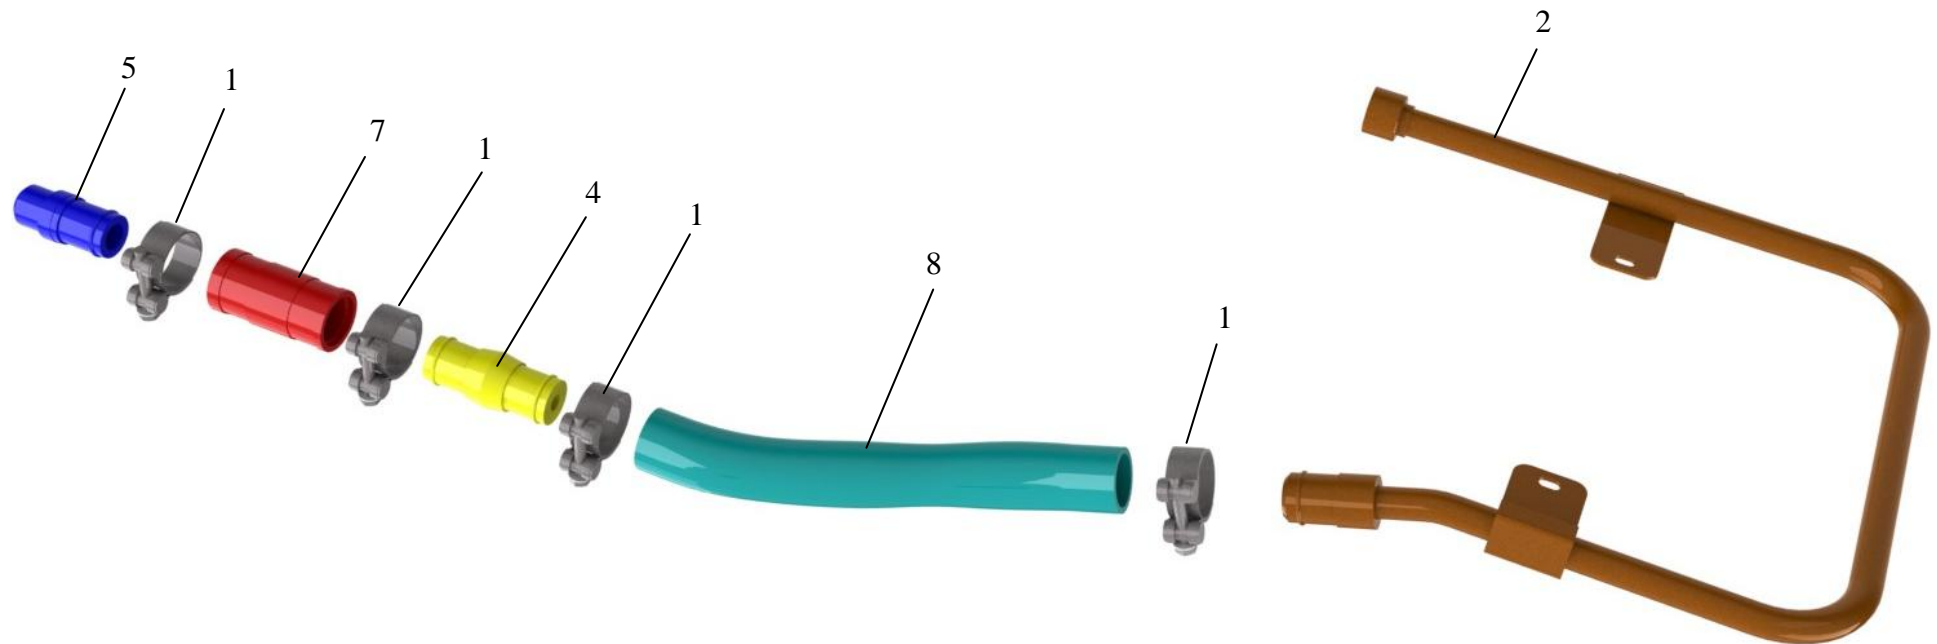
Труба компрессора АКСМ 32102-230303.000
